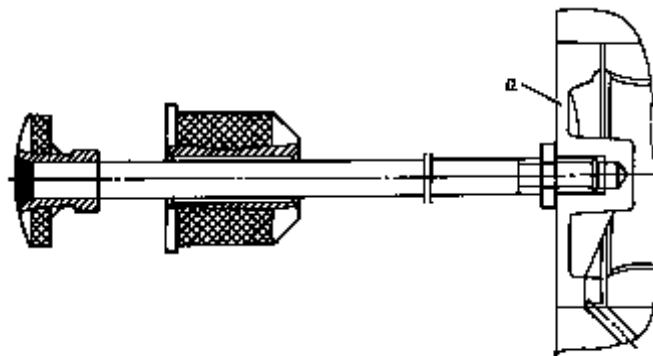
Приспособление для выпрессовки заглушки поршня
